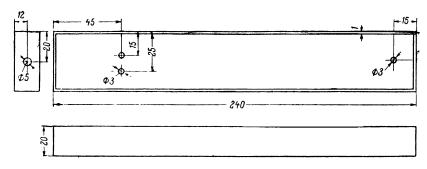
Чертеж корпуса дуплексной радиостанции.
